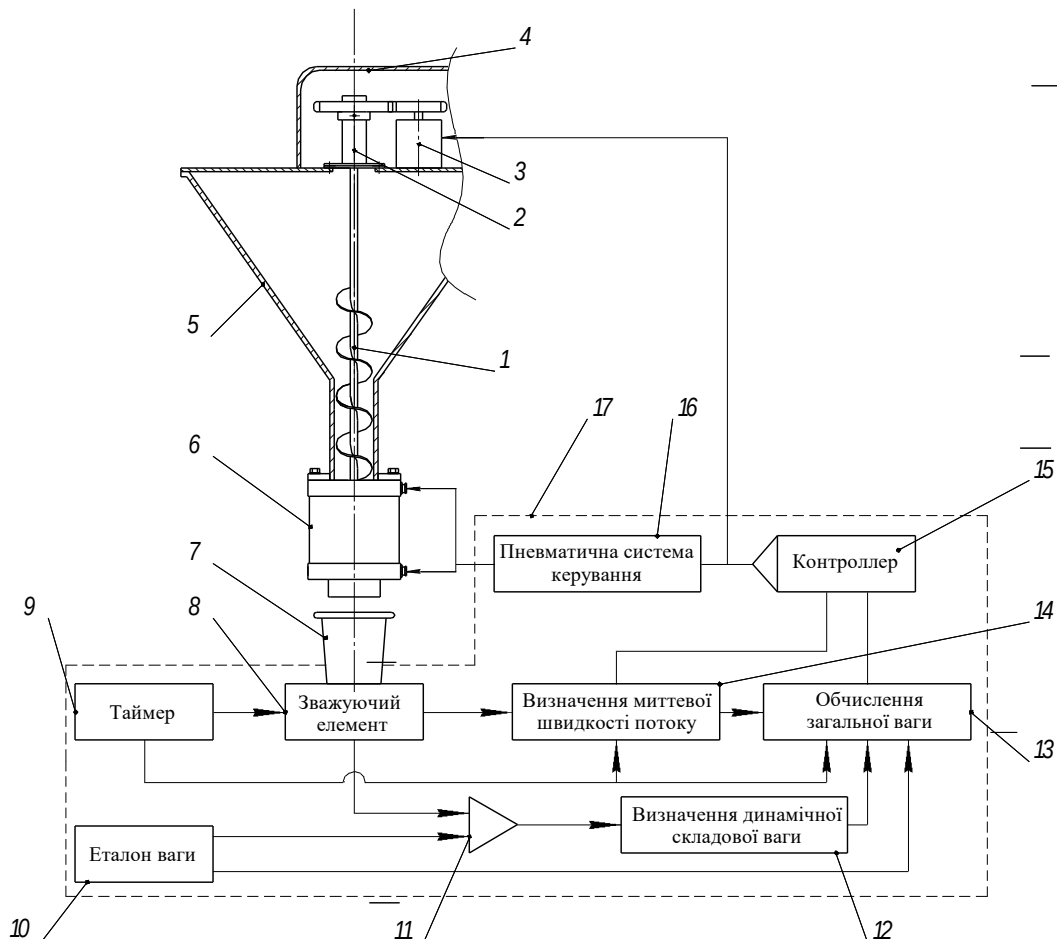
Схема мехатронного модуля вагового дозування пластичної продукції: 1 - шнек; 2 - приводний механізм; 3 – привід; 4 - кришка; 5 - бункер; 6 – телескопічний патрубок; 7 - тара; 8 – зважувальний елемент; 9 - таймер; 10 - еталон ваги; 11 - компаратор; 12 – блок визначення динамічної складової ваги; 13 - блок обчислення загальної ваги; 14 - блок визначення миттєвої швидкості потоку; 15 - контролер; 16 – пневматична система керування; 17 – система керування
